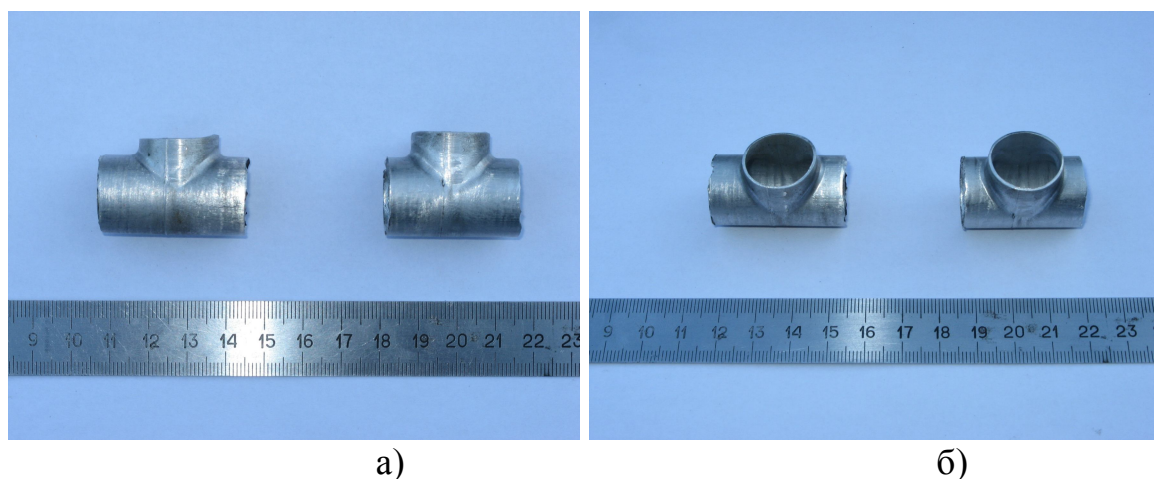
Образцы полученных деталей: а) вид сбоку; б) вид сверху
